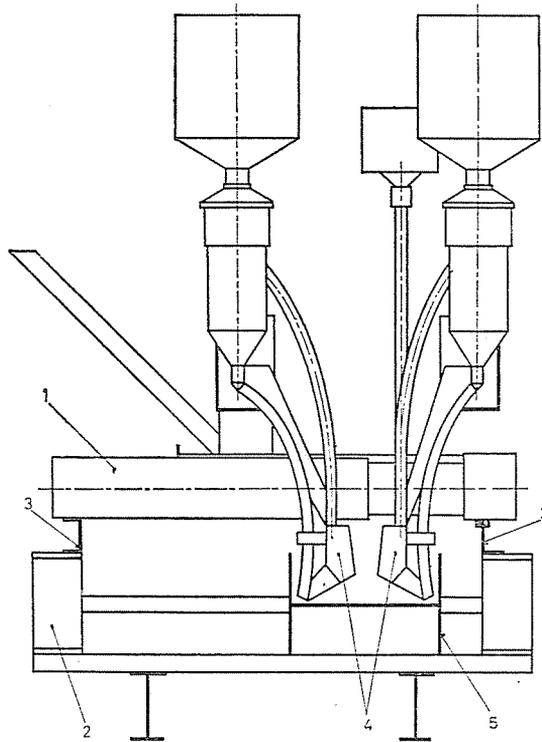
Schweißautomat ESAB A6: 1 Laufwerk; 2 Schweißgestell; 3 Führungsbahnen; 4 Schweißköpfe; 5 I-Träger
